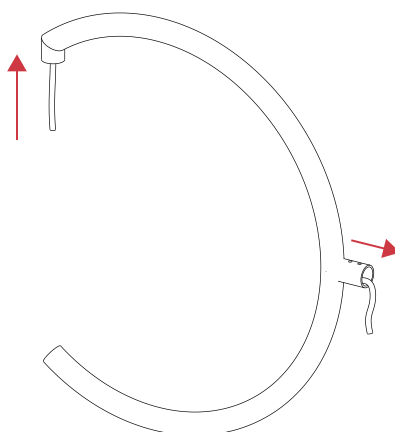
Instalación del cableado por el interior de la estructura de la lámpara de pared.
